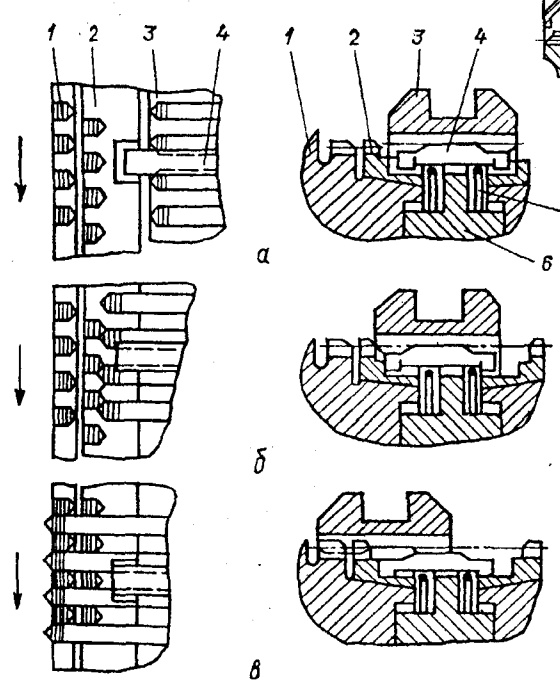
Схема работы синхронизатора: 1 – зубчатый венец шестерни; 2 – блокирующее кольцо синхронизатора; 3 – муфта синхронизатора; 4 – сухарь синхронизатора; 5 – пружина синхронизатора; 6 – ступица синхронизатора; а – нейтральное положение передач; б – начало синхронизации; в – передача включена
